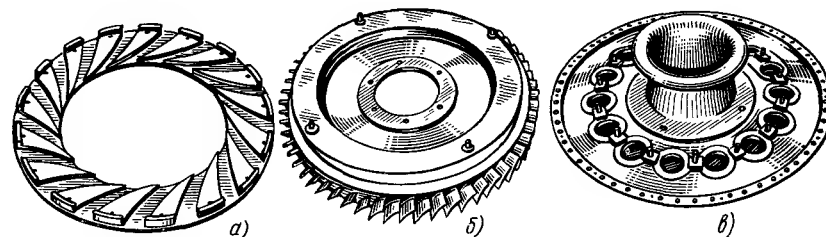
Лопаточные диффузоры напорных патрубков компрессоров:
